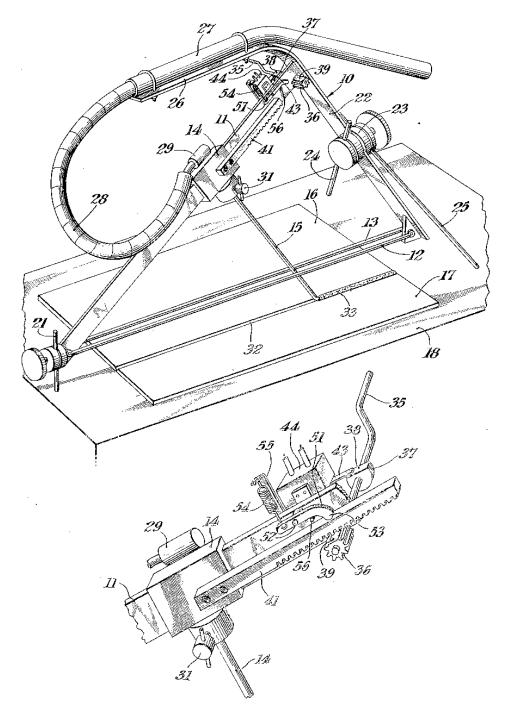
Устройство для сварки наклонным электродом и электрододержатель
